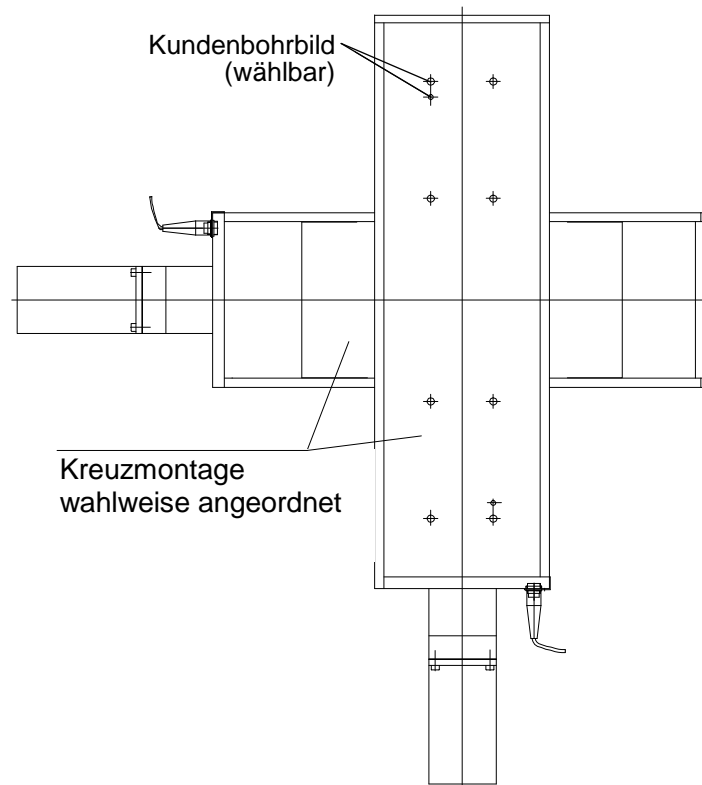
Linearschlittensysteme kreuzmontiert mit Befestigungsbohrungen
